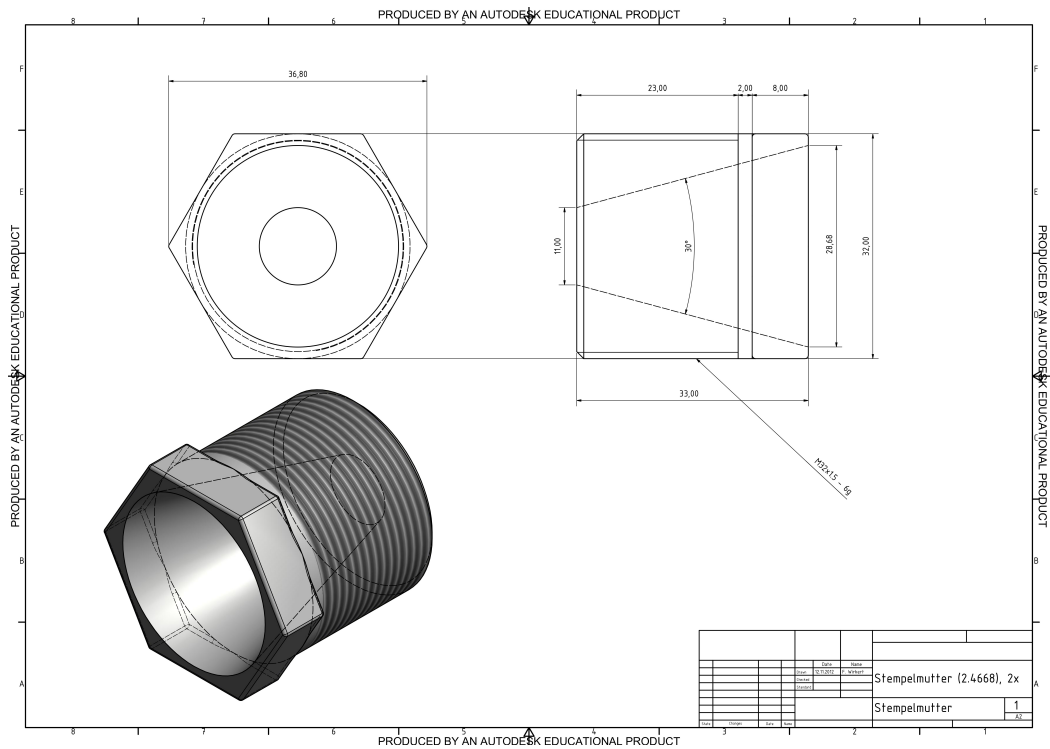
Technische Zeichnung Diamant-Stempel-Schraube
